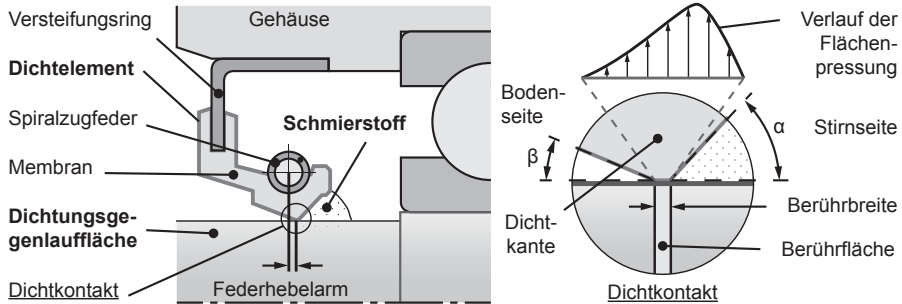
Radialwellendichtung nach DIN 3760 Bauform B [10]; Rechts: Detailansicht des Dichtkontakts
